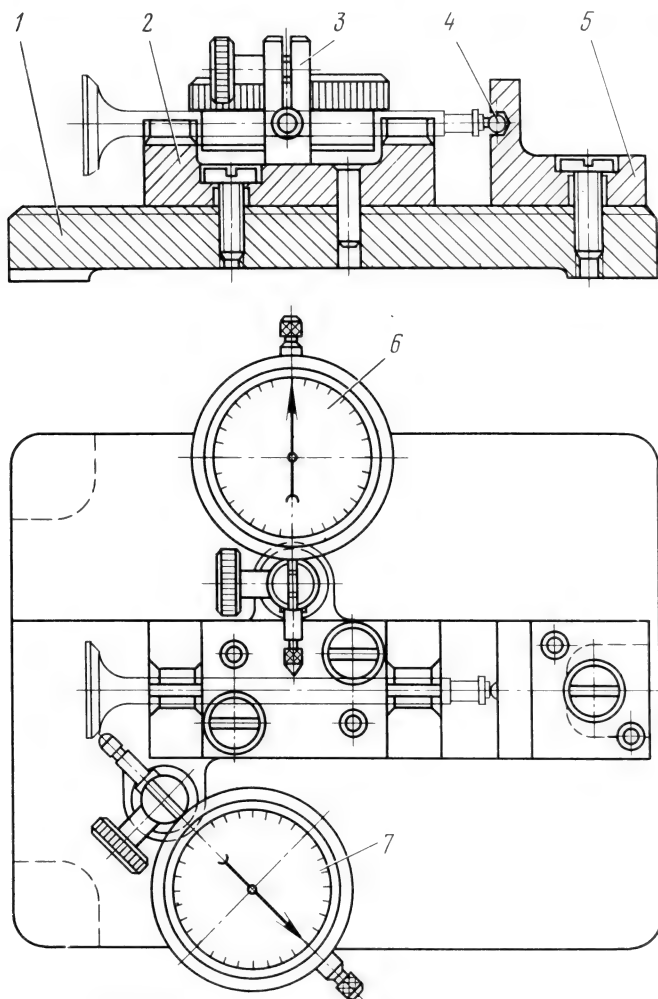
Проверка клапана на concentricity рабочей фаски головки и стержня:
